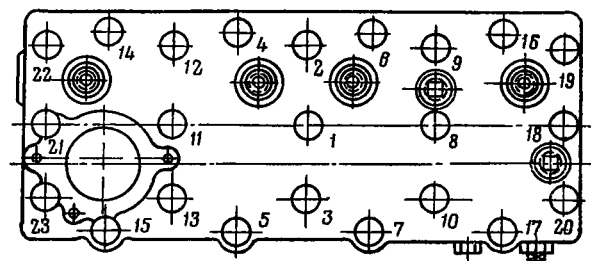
Порядок затяжки гаек шпилек крепления головки блока цилиндров
